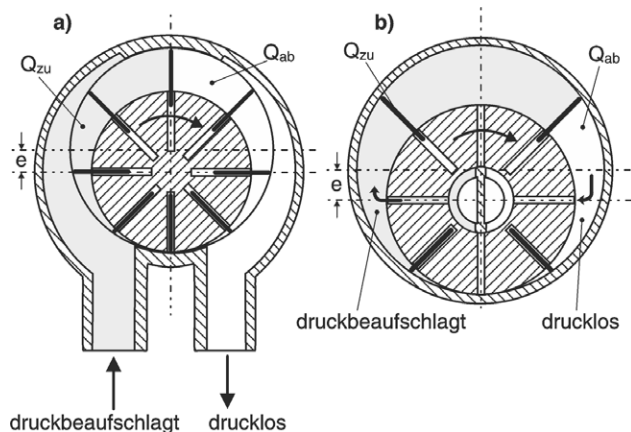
Flügelzellenmotor a) außen beaufschlagt
